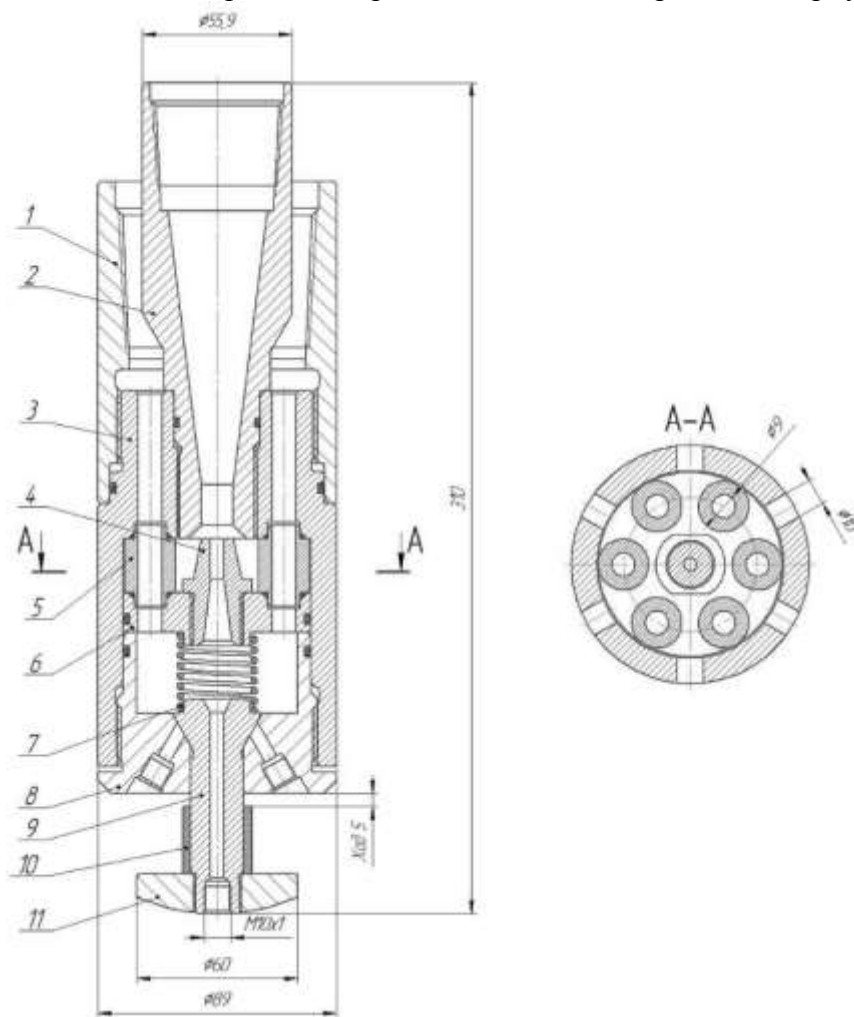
Сборочный чертеж погружной эжекционной установки: 1 – муфта; 2 – диффузор; 3 – корпус; 4 – сопло; 5 – втулка; 6 – распределитель; 7 – пружина; 8 – размывочная головка; 9 – шток; 10 – втулка; 11 – опора
